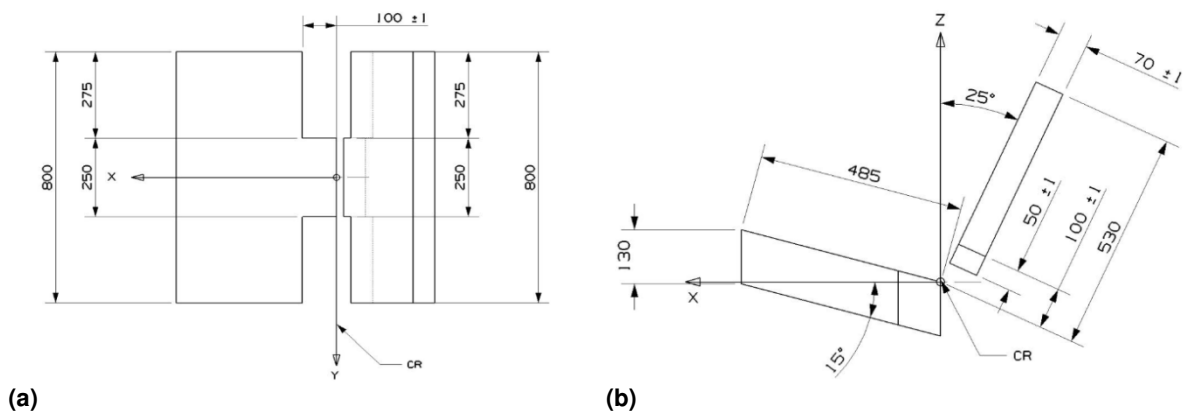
Dimensions de la banquette d'essai : (a) vue du dessus ; (b) vue de coupe. UNECE, 2013 [122]
